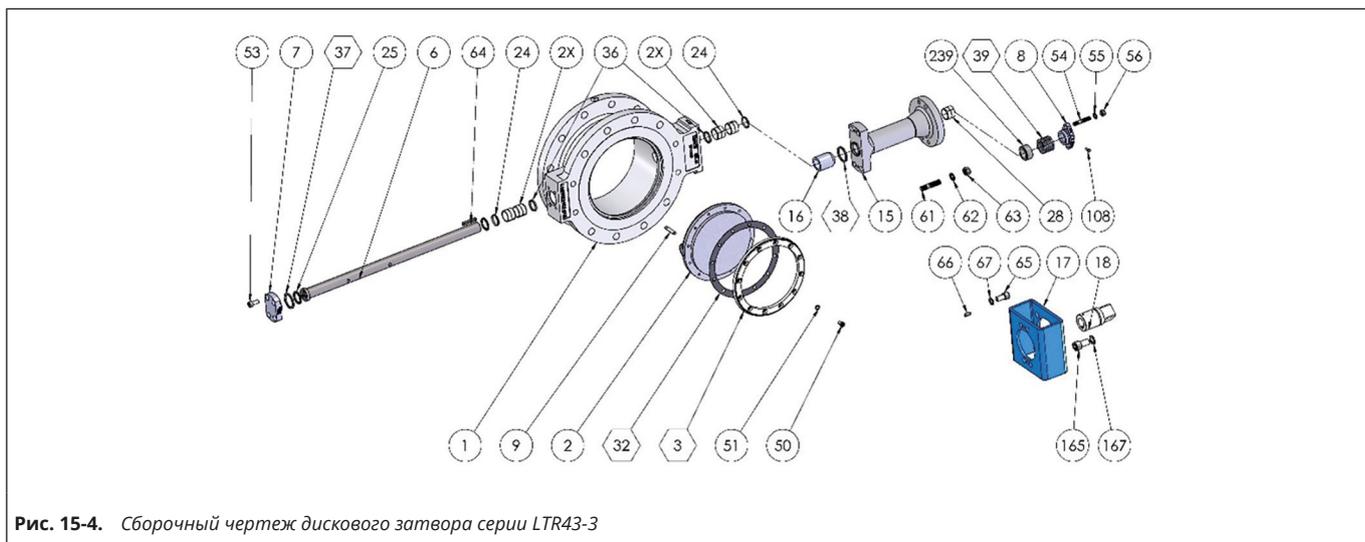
Сборочный чертеж дискового затвора серии LTR43-3
